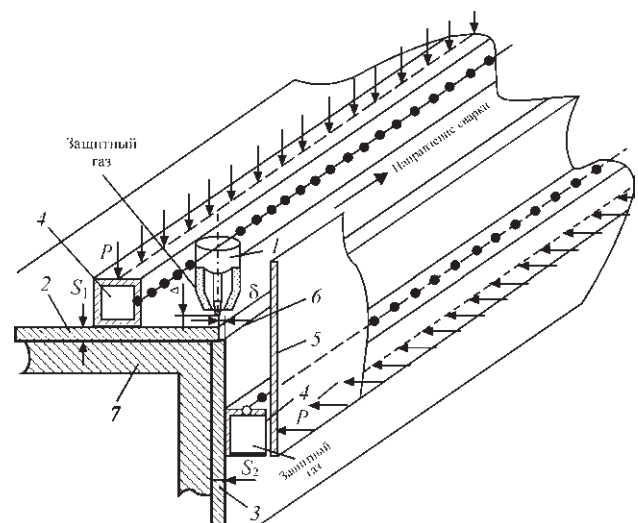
Схема ведения сварочной горелки по стыку: 1 — сварочная горелка; 2, 3 — свариваемые заготовки; 4 — газовый канал для защиты внешней стороны изделия; 5 — защитный экран; 6 — газовый канал для защиты обратной стороны шва изделия; 7 — силовая часть оснастки
